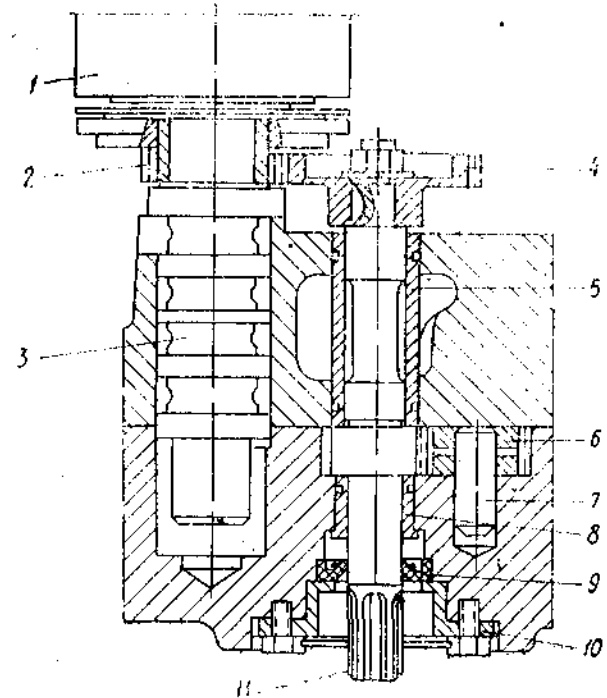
Привод измерителя скорости: 1—измеритель скорости; 2—шестерня измерителя скорости; 3—бухса золотника; 4—ведущая шестерня; 5—втулка; 6—ведомая шестерня масляного насоса; 7—ось шестерни; 8—втулка; 9—манжета; 10—крышка; 11—валик
